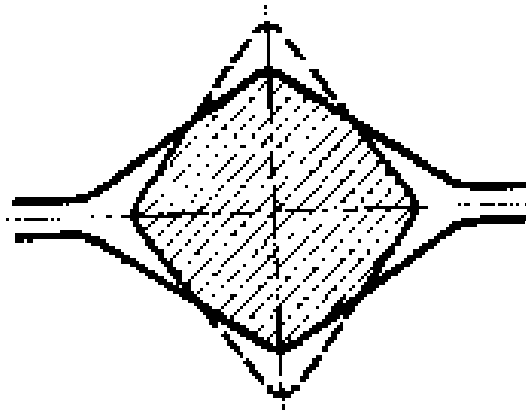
Схема отримання квадратної заготовки в ромбічну калібри
